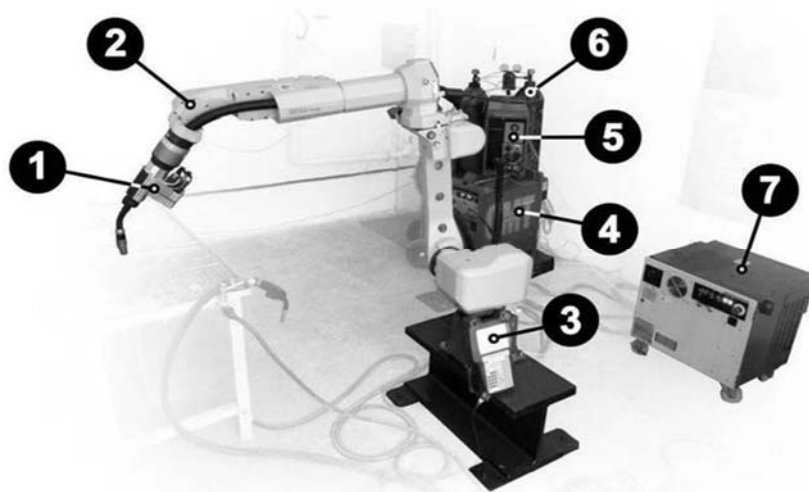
Установка для сварки плавлением с использованием технологии СМТ
